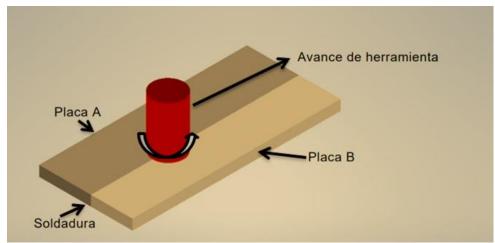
Proceso de soldadura por fricción y agitación.
